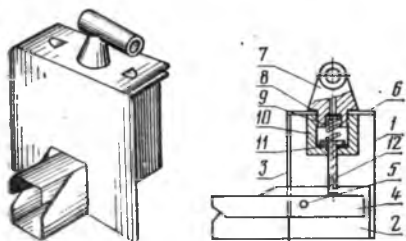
Автопоилка АНК: 1 — стойка; 2 — корыто; 3 — щиток; 4 — рычаг; 5 — ось; 6 — крышка; 7 — тройник; 8 — прокладка; 9 — пружина; 10 — колпачок; 11 — резиновая шайба; 12 — клапан.
